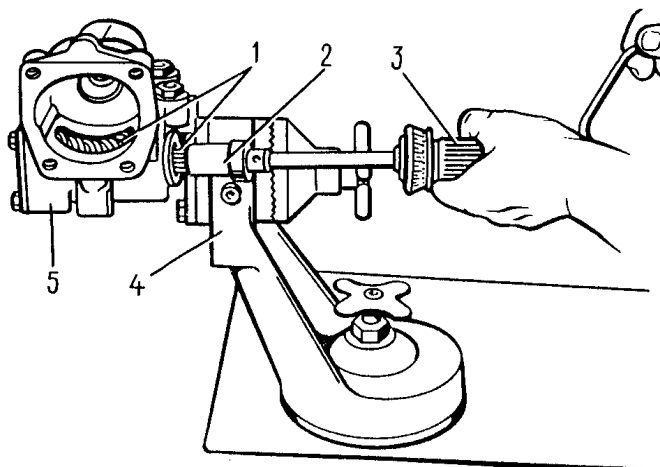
Remoción del anillo exterior del cojinete superior del sinfín con ayuda del extractor 67.7853.9541:
